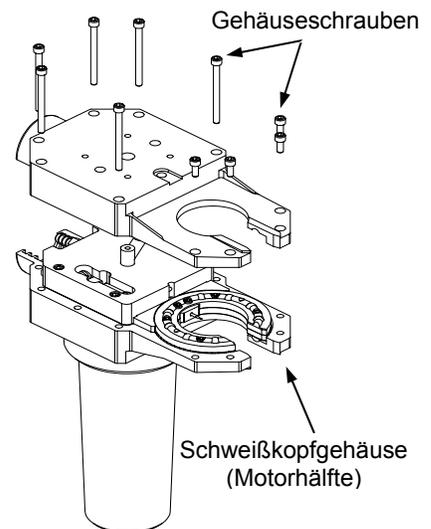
Entfernen des Halteringhälfte des Schweißkopfgehäuses
